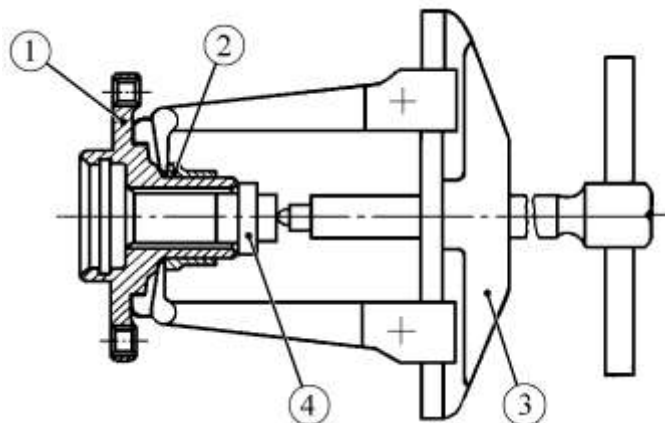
Спрессовка внутреннего кольца подшипника со ступицы переднего колеса:
